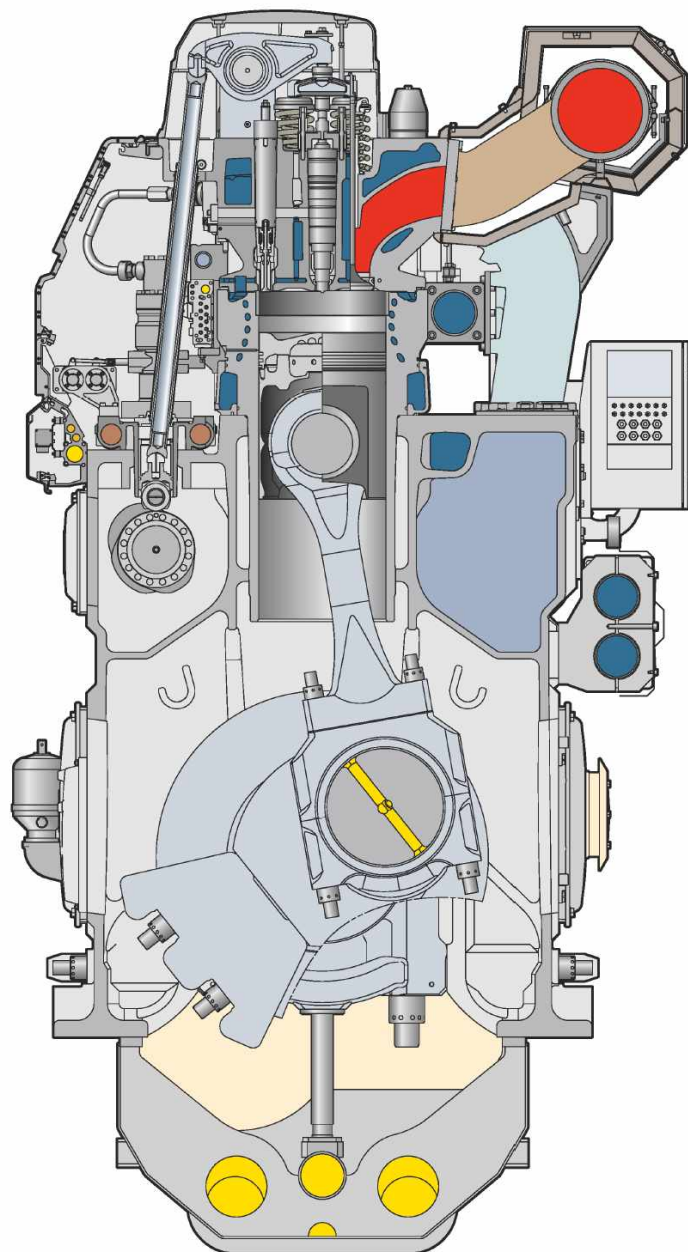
Поперечний переріз двигуна 9ЧН46/58
